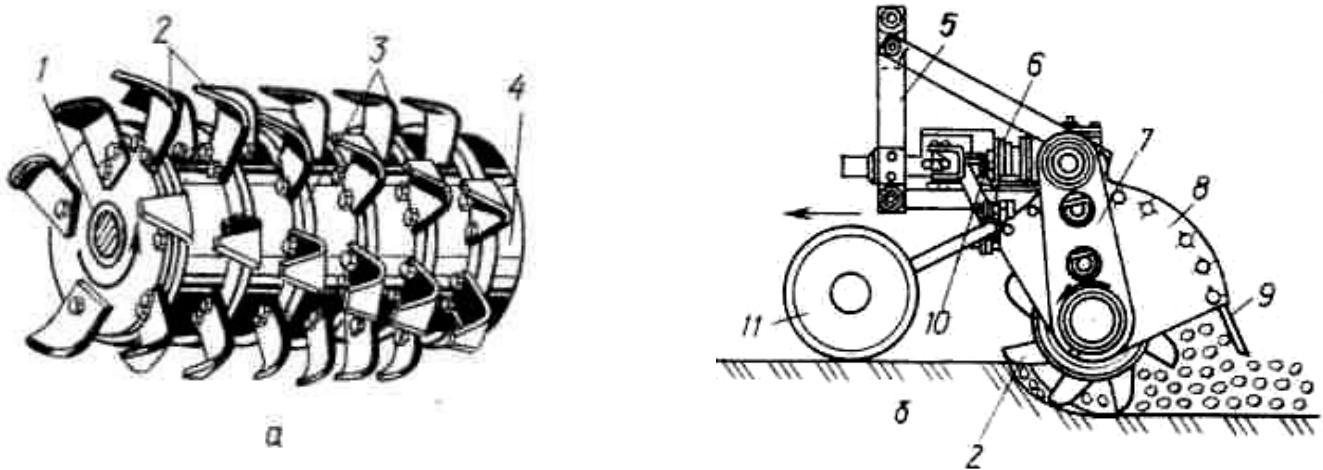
Фреза болотна напіпна ФБН-1,5:
